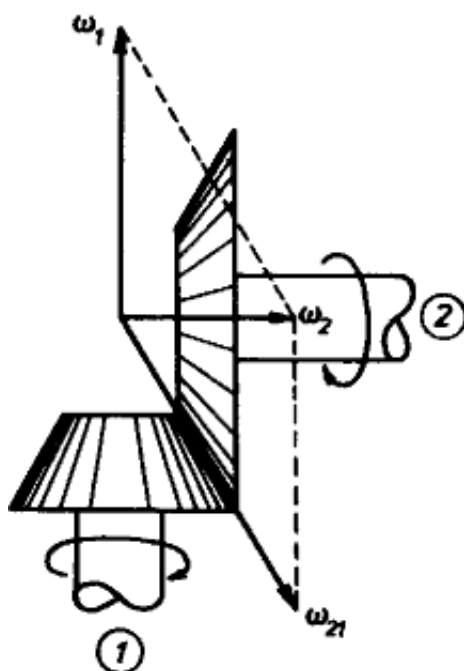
Engranaje cónico con ángulo entre ejes igual a 90°
